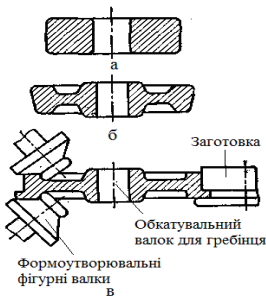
Схема отримання заготовки вагонного колеса: а – поковка; б – штампована поковка; в – розкатування
